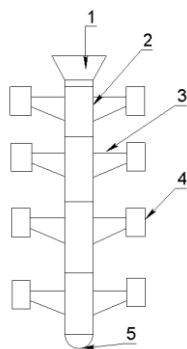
Блок отливок: 1 - литниковая чаша; 2 - стойки; 3 - питатели; 4 - отливки; 5 - зумпф.
